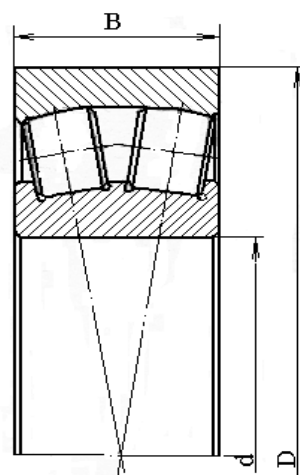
Подшипник роликовый радиальный, двухрядный, самоустанавливающийся с бочкообразными роликами
